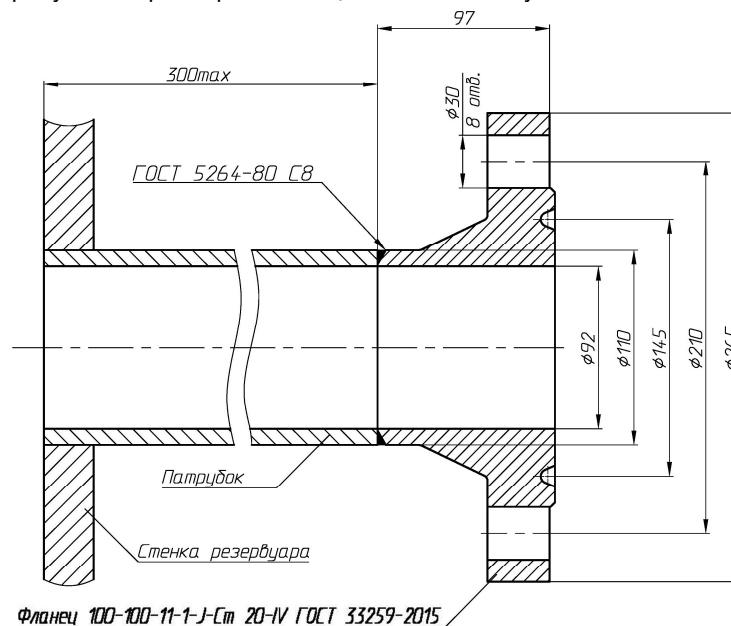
Рекомендуемый вариант посадочного места для установки фланца на резервуар
